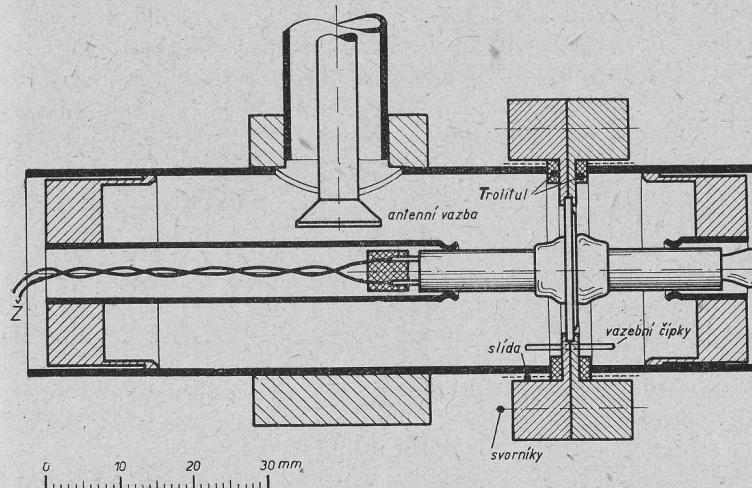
Mechanické provedení oscilátoru s elektronkou 5794 pro kmitočet 1250 MHz.
